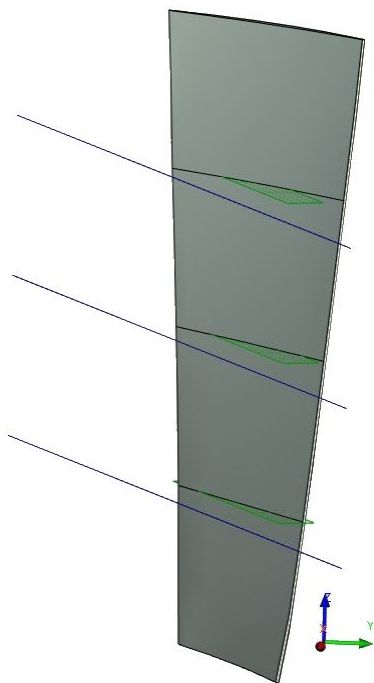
3D-профиля для разделения корытца лопатки
